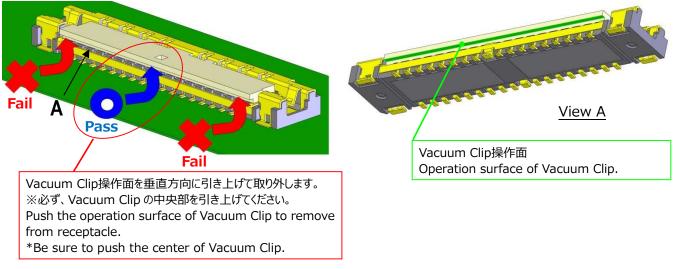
Vacuum Clip 取り外し方法 How To Remove Vacuum Clip
